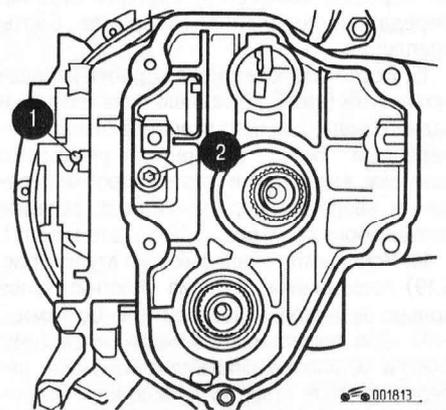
Расположение болтов крепления держателя вала передачи заднего хода: 1 – наружный болт; 2 – внутренний болт
